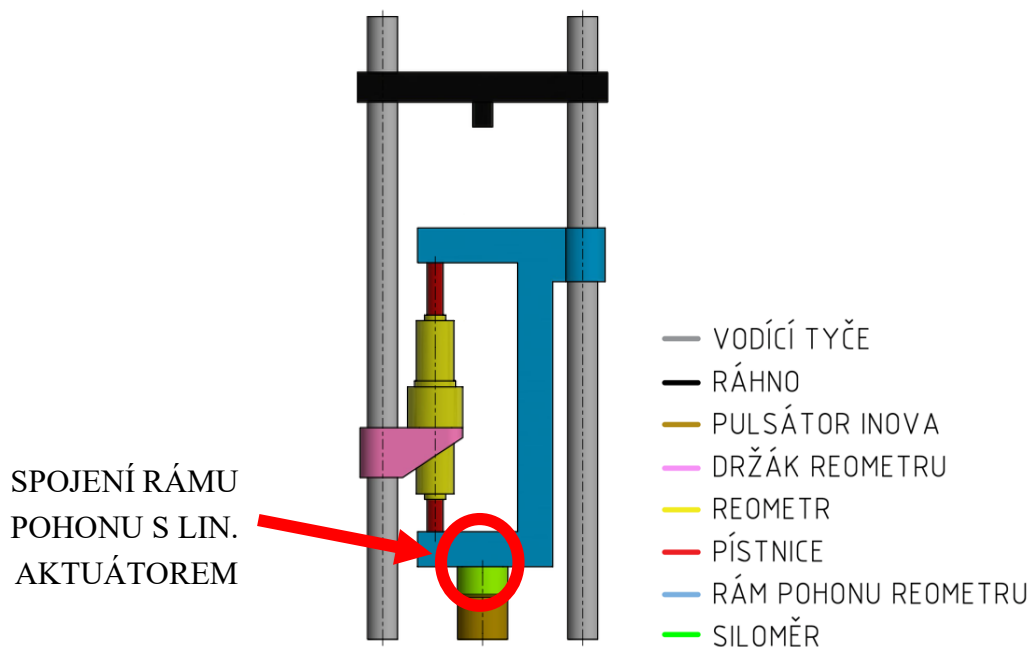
Posuvný mechanismus se svěrným spojením
